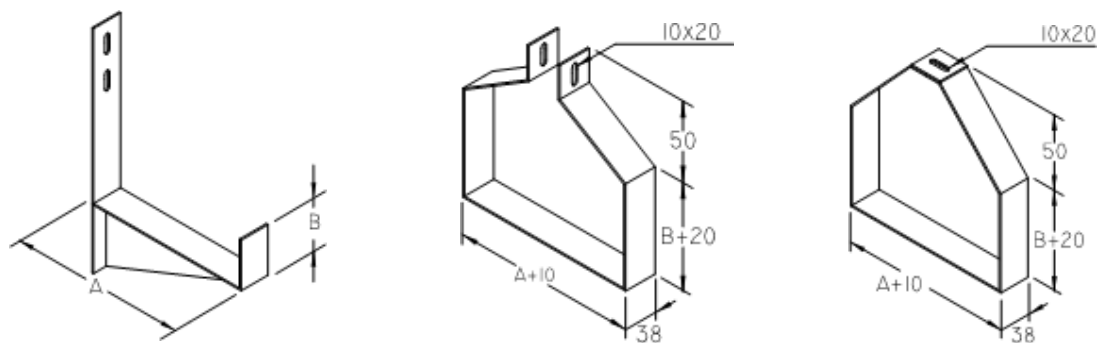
Suporte reforçado, gancho horizontal e gancho vertical
